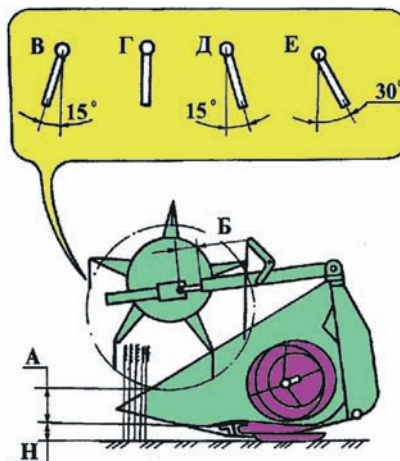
Схема установки мотовила при работе жатки. А-величина расположения по высоте граблин; Б-величина выступающей части штока гидроцилиндра перемещения мотовила по горизонтали; В, Г, Д, Е-положения граблин, Н-высота среза стеблей
